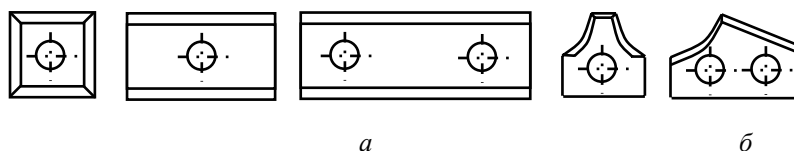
Режущие пластины: *a* – поворотные; *б* – профильные
